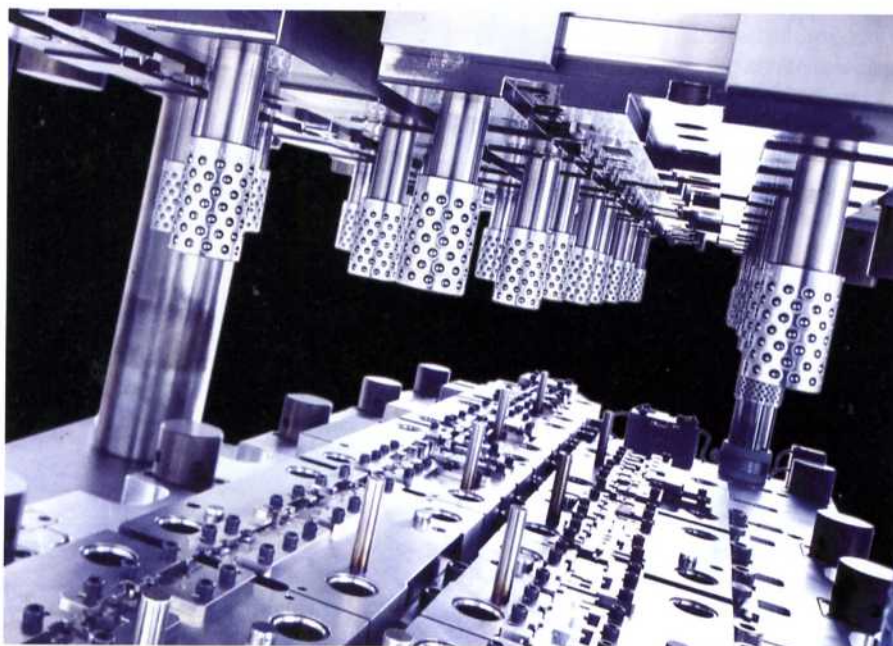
Schroeder+Bauer fertigt mit hoher Präzision und Zuverlässigkeit Umformwerkzeuge für Crimp- und Einpresskontakte.
